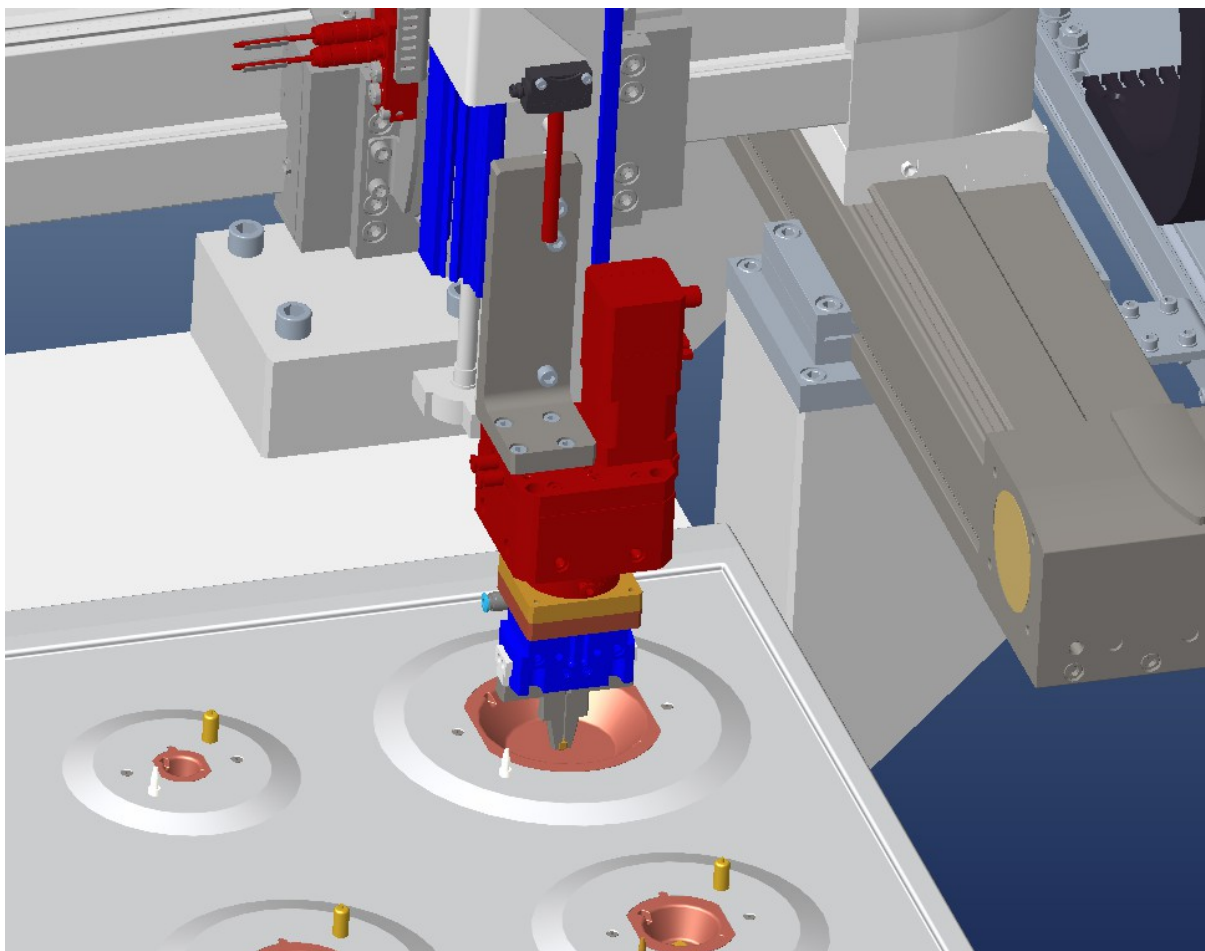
Chapač pro odebrání a šroubování trysek do hořáků
